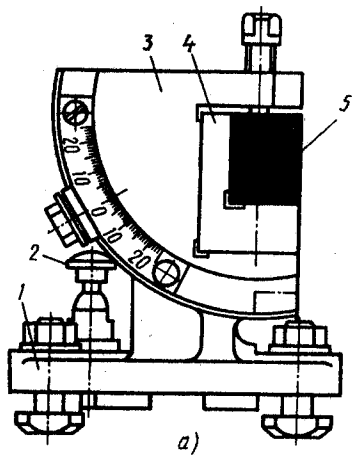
Приспособления для закрепления резцов на затачном станке мод. 3629
